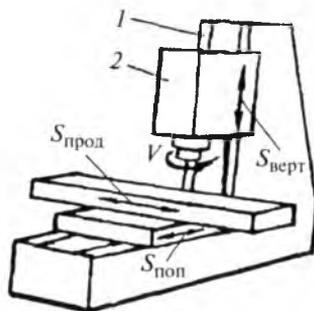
Вертикально-фрезерный бесконсольный станок:
